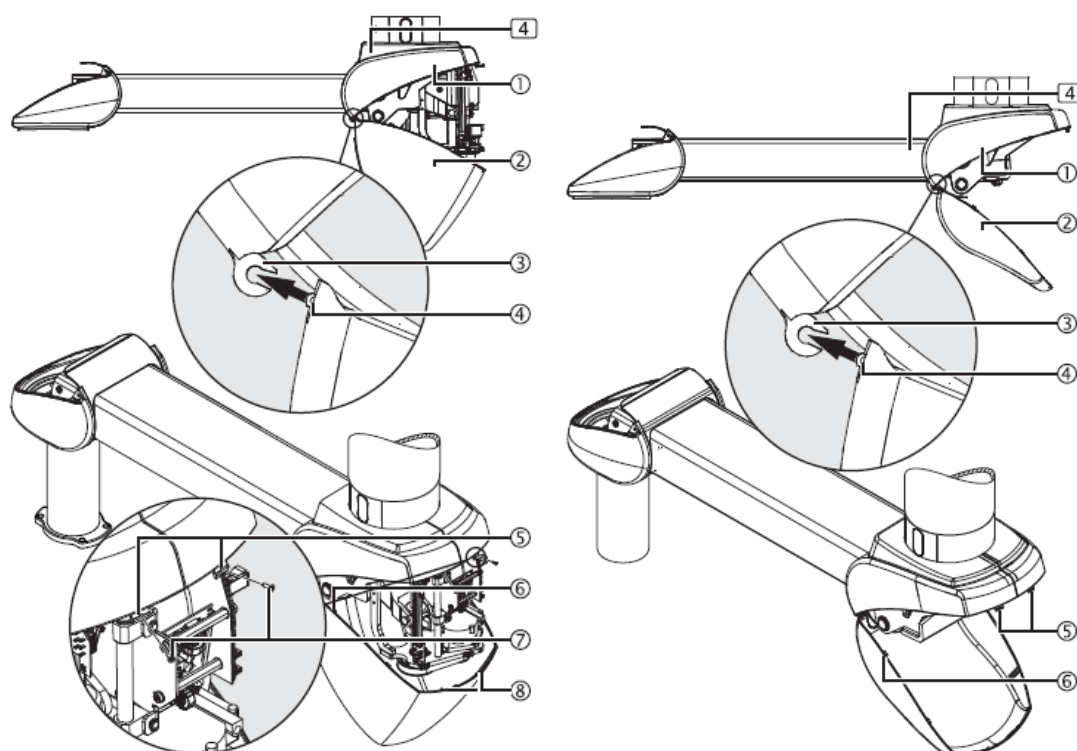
Montage du couvercle inférieur arrière sur un bras de ressort ou de moteur
